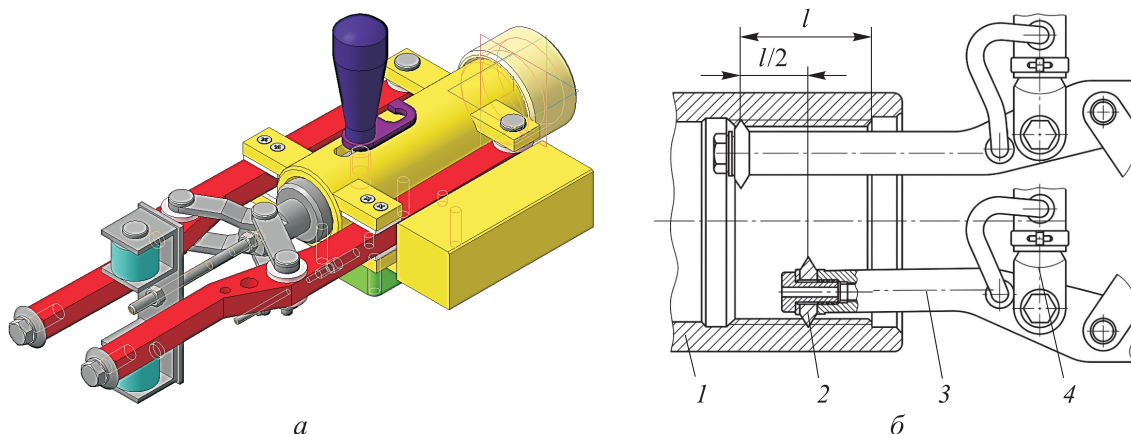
Внешний вид державки (а) и принципиальная схема (б) ЭМО резьбы
